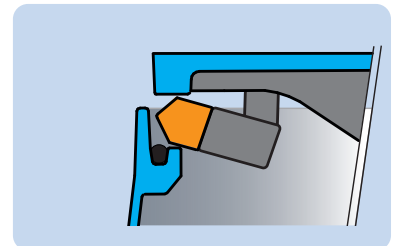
Federstab verbogen: Position zu nah an Deckelunterseite und zu weit außen, Deckel lässt sich nicht schließen
